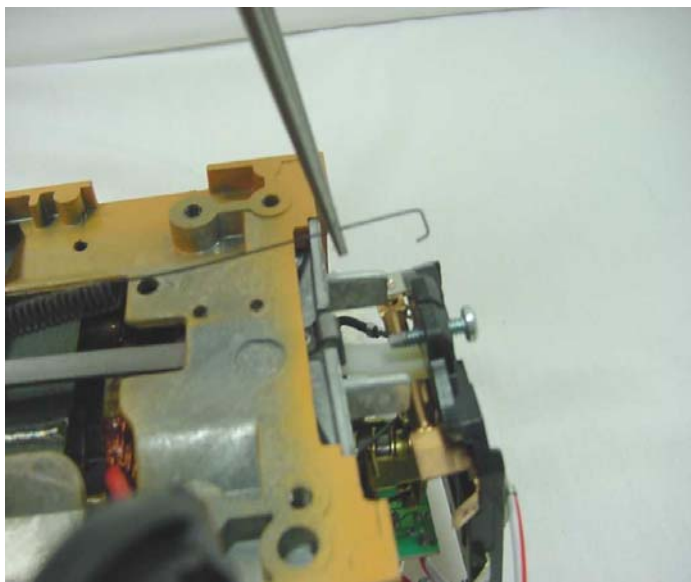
Feder der Kontrollplatte mit einer Zange in die untere Bohrung einhängen.
